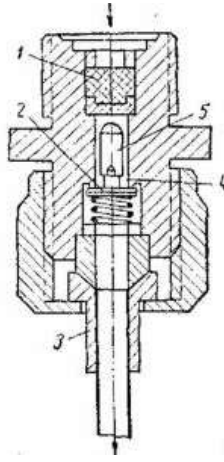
Дозирующий клапан для централизованной жидкой смазки.
